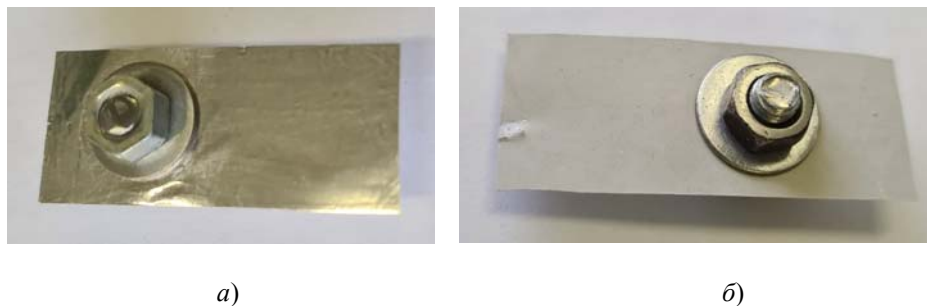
Исходный конструктивно-подобный образец без покрытия (а) и с покрытием (б)
